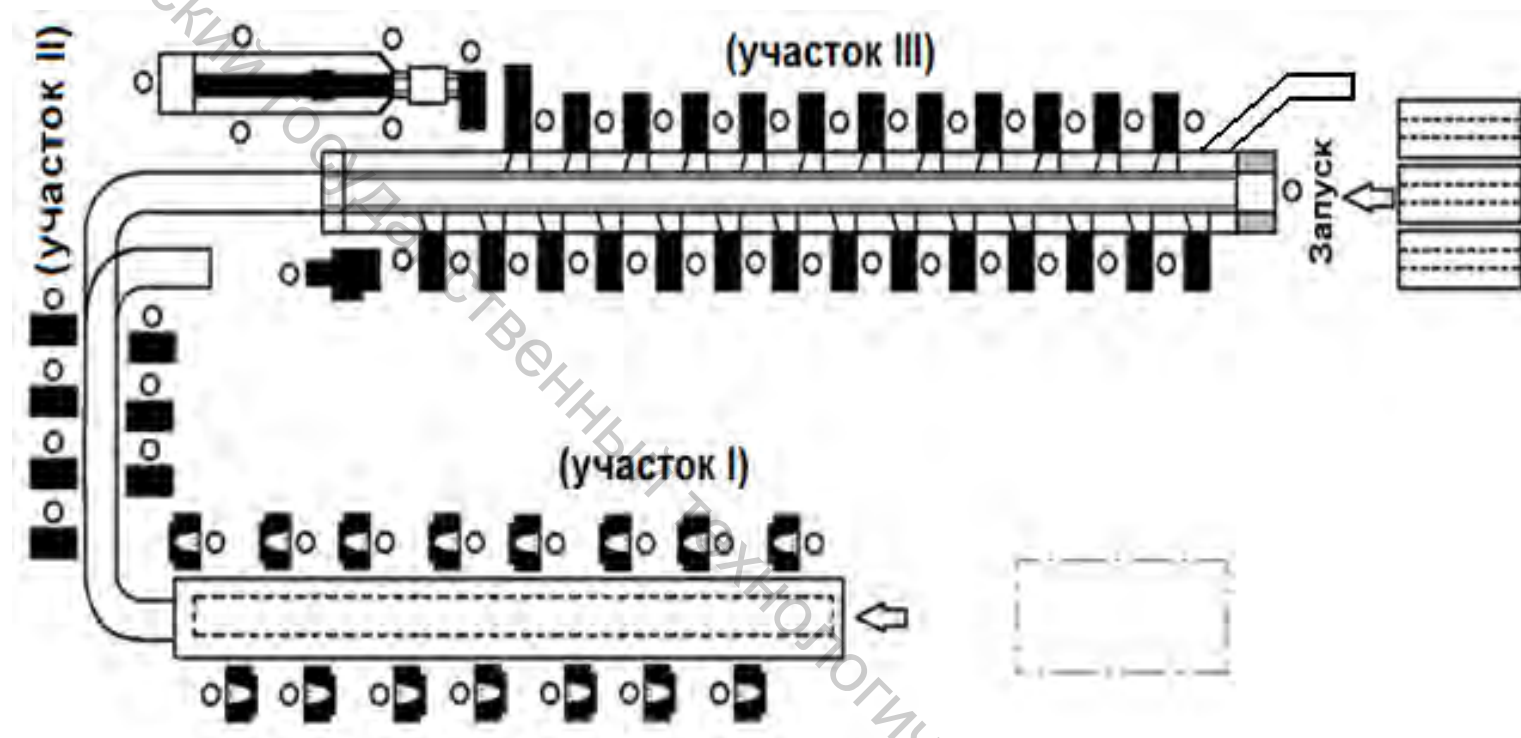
Схема соединения транспортных средств раскройно-заготовочного цеха с компоновкой оборудования
